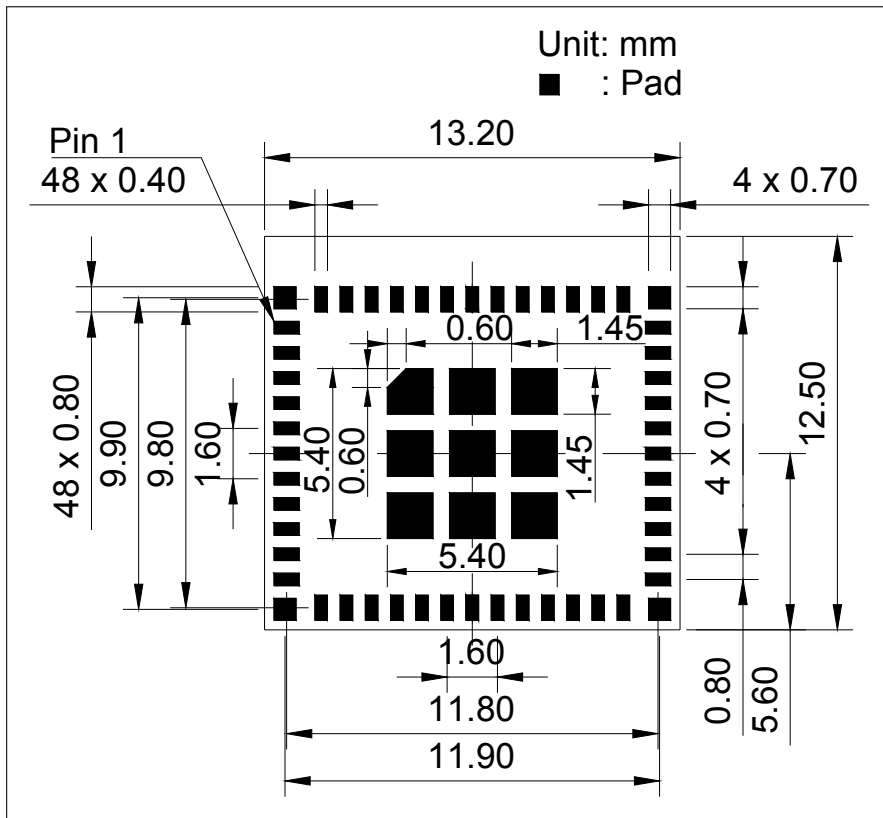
ESP32-C6-MINI-1U 推荐 PCB 封装图形
